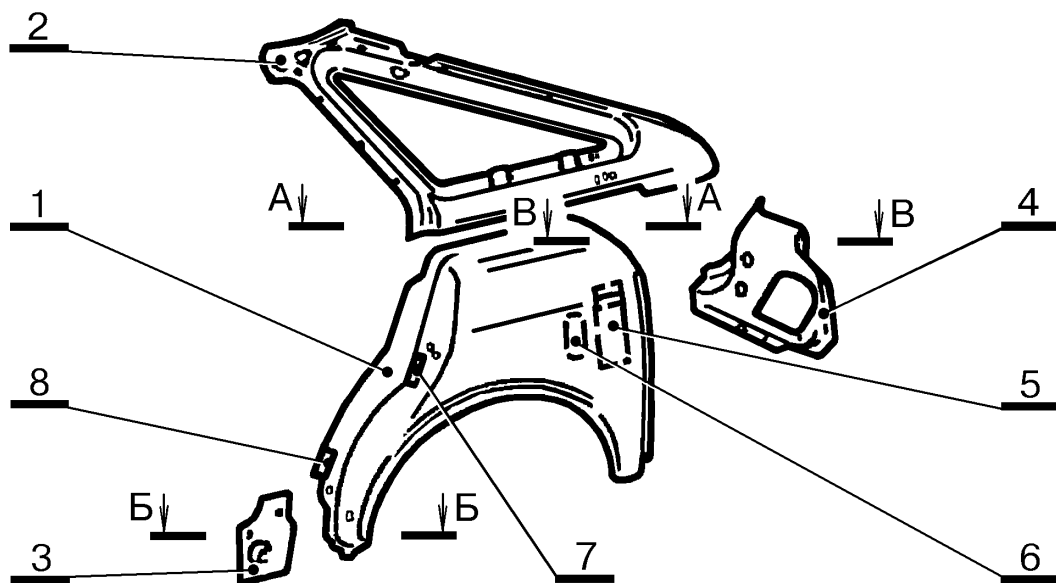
Детали арки ВАЗ-2112 заднего колеса наружной с угловой панелью боковины в сборе правой/левой. Номера и наименования деталей, количество сварочных точек приведены в таблице 12.
